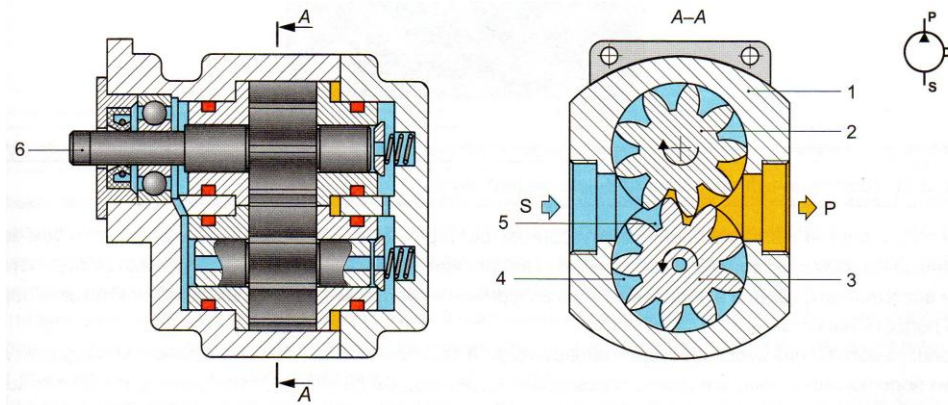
, б. Схема шестеренного насоса с внешним зацеплением: 1- корпус; 2, 3 – две одинаковые прямозубые цилиндрические шестерни; 4 – рабочая жидкость; 5 – камера всасывания; 6 – вал ведущей шестерни насоса, связывающийся муфтой с валом приводного электродвигателя.
